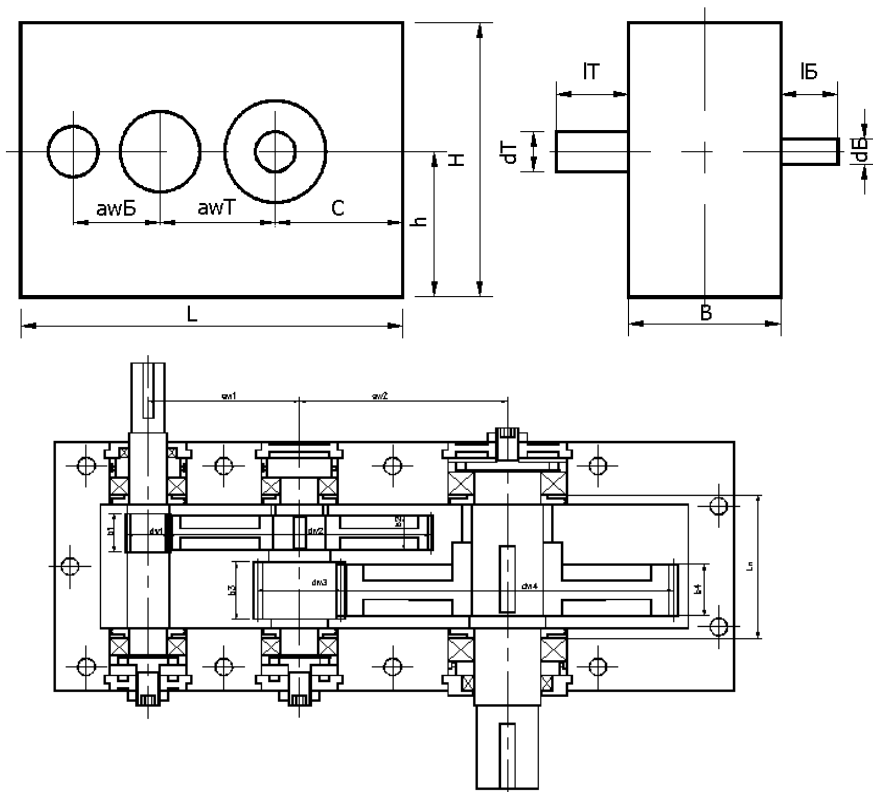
Габаритный чертеж и компоновка передач двухступенчатого цилиндрического редуктора типа Ц2У по ГОСТ 20758-75. К заданиям №№ 1...5.
